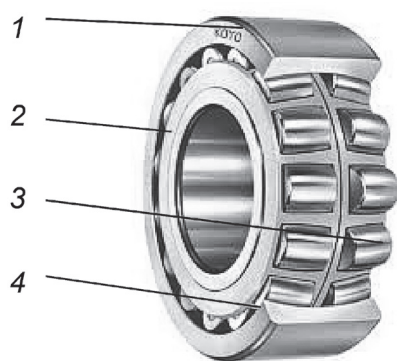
Внешний вид двухрядного роликового подшипника качения Минского подшипникового завода: 1 – внешнее кольцо; 2 – внутреннее кольцо; 3 – сепаратор; 4 – тела качения
